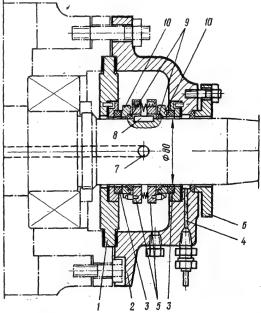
Сальник пружинный уплотнения конца вала (компрессора AV200):
